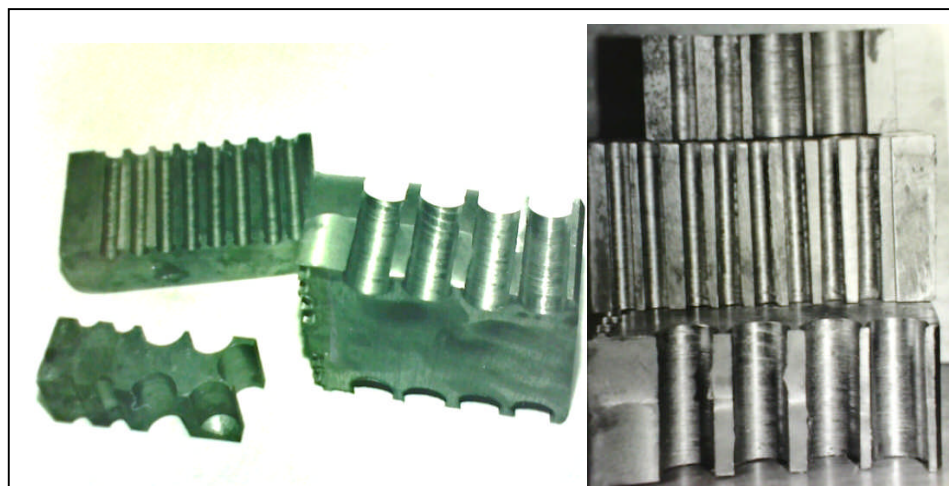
Eprouvettes découpées pour mesurer la rugosité de la surface usinée.
